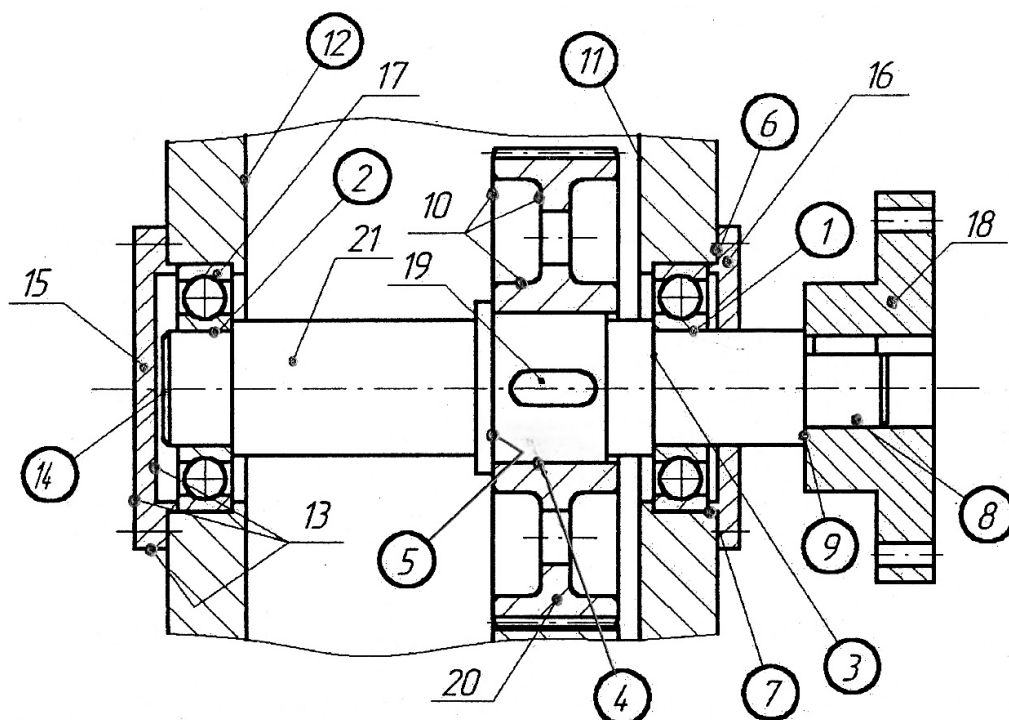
Поверхні деталей ступеня редуктора
